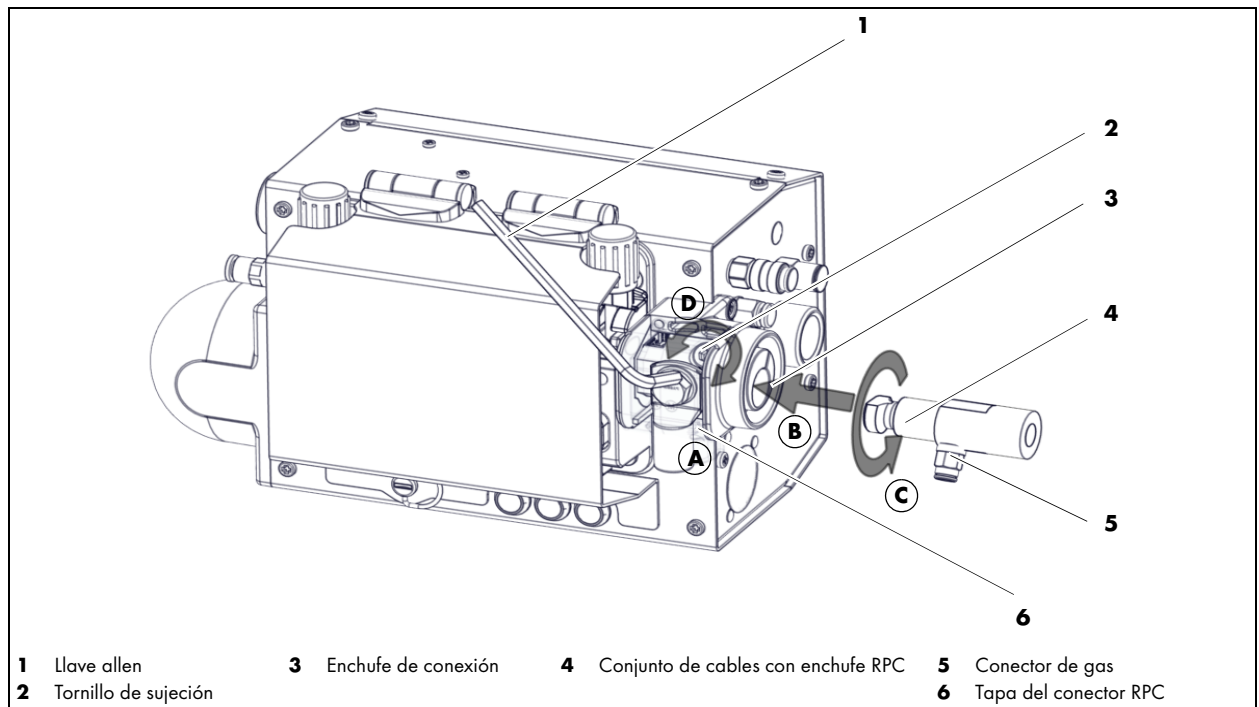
Conjunto de cables de la antorcha de soldadura (conector RPC) iROB Feed 22 (versión con devanadora o alimentador montado a la derecha)
